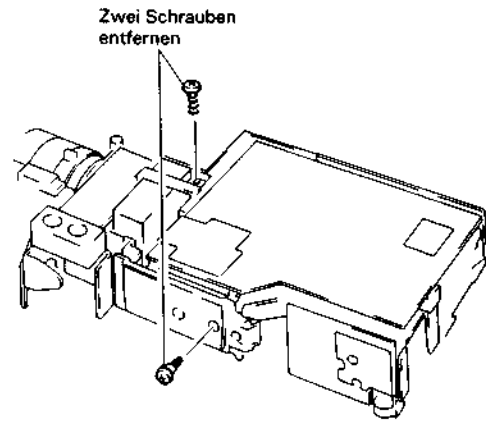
Ausbau der Sensor-Leiterplatte
